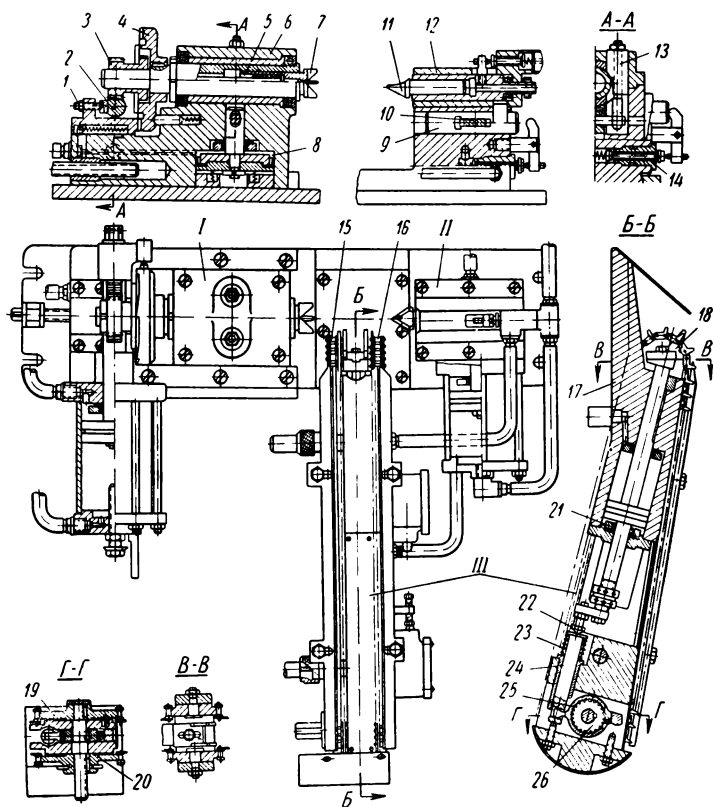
Зажимное приспособление с цепным транспортером для обработки деталей с центровыми гнездами
